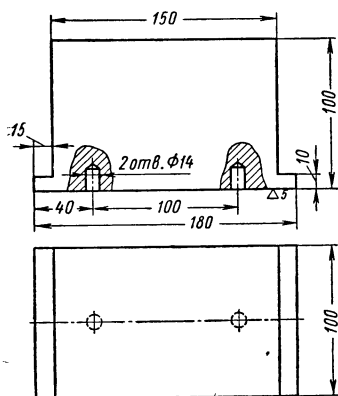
Чертеж обрабатываемой детали постоянной ширины
